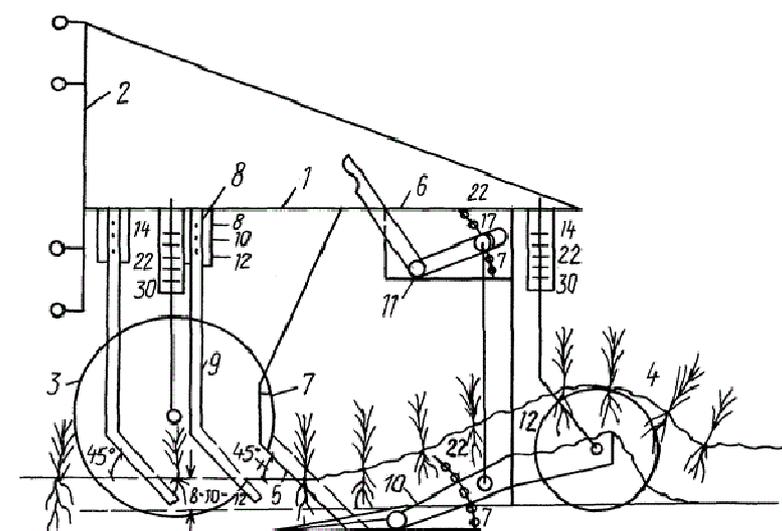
Схема машины для выкопки саженцев по патенту РФ 2172576 [2]:
